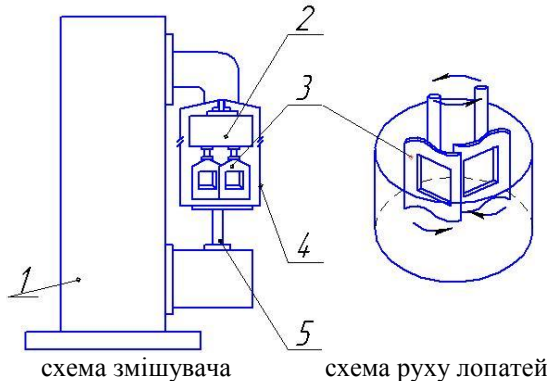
Схема планетарного змішувача з вертикальними лопатями:
